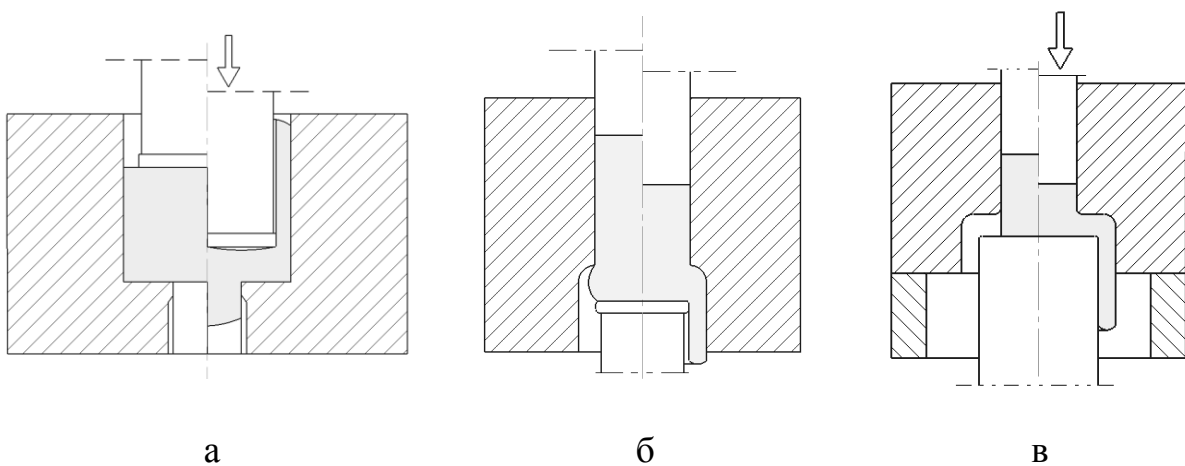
Схеми комбінованого видавлювання деталей типу стаканів з зовнішніми відростками
